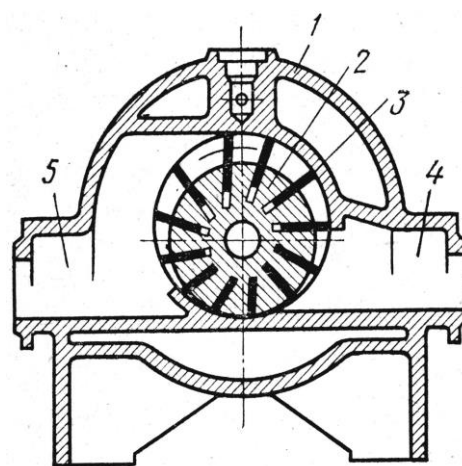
Многопластинчатый насос: 1 — корпус; 2 — ротор; 3 — подвижные пластины; 4 — выпускной патрубок; 5 — входной патрубок
